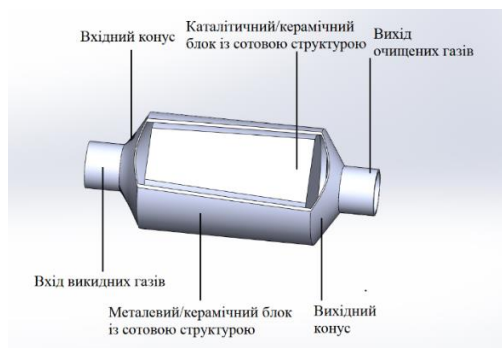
Принципова схема каталітичного нейтралізатора
